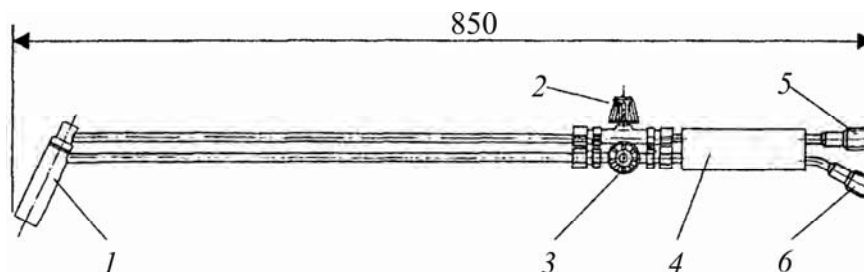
Горелка ПВ-1: 1 — головка горелки; 2 — вентиль подачи воздуха; 3 — вентиль подачи горючего; 4 — державка; 5 — штуцер воздуха М 16 × 1,5; 6 — штуцер горючего М 16 × 1,5 Н
